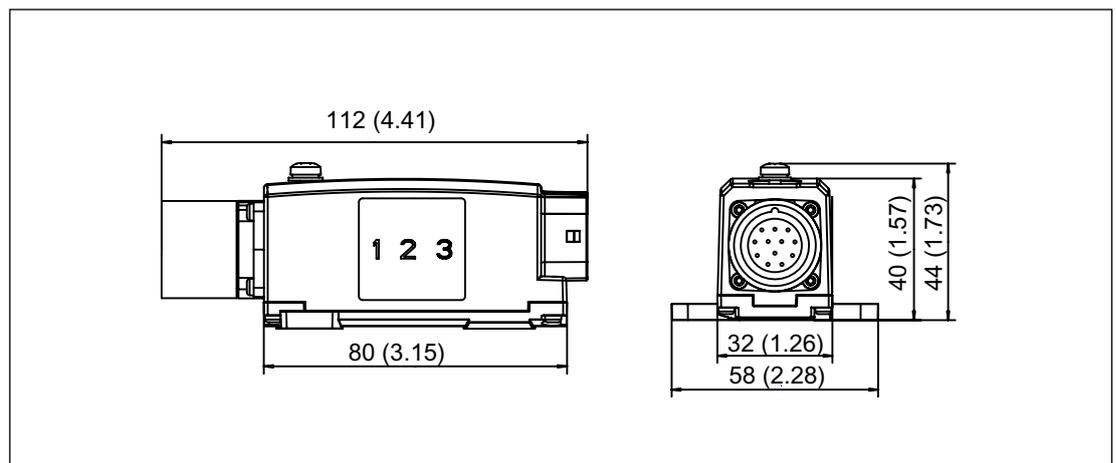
Maßbild SME20, Bestellnummer 6SL3055-0AA00-5EA3
